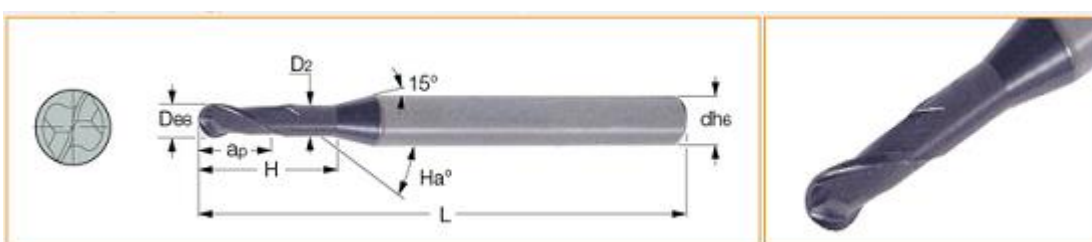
Stopková fréza T290 ELN D08-01-C08-05 [12].
